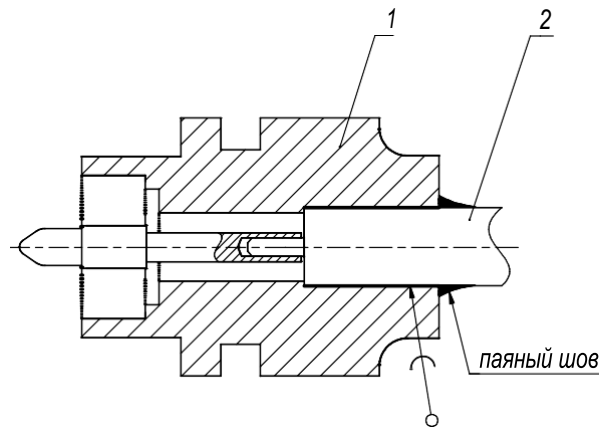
Монтаж кабеля к корпусу кабельного соединителя
